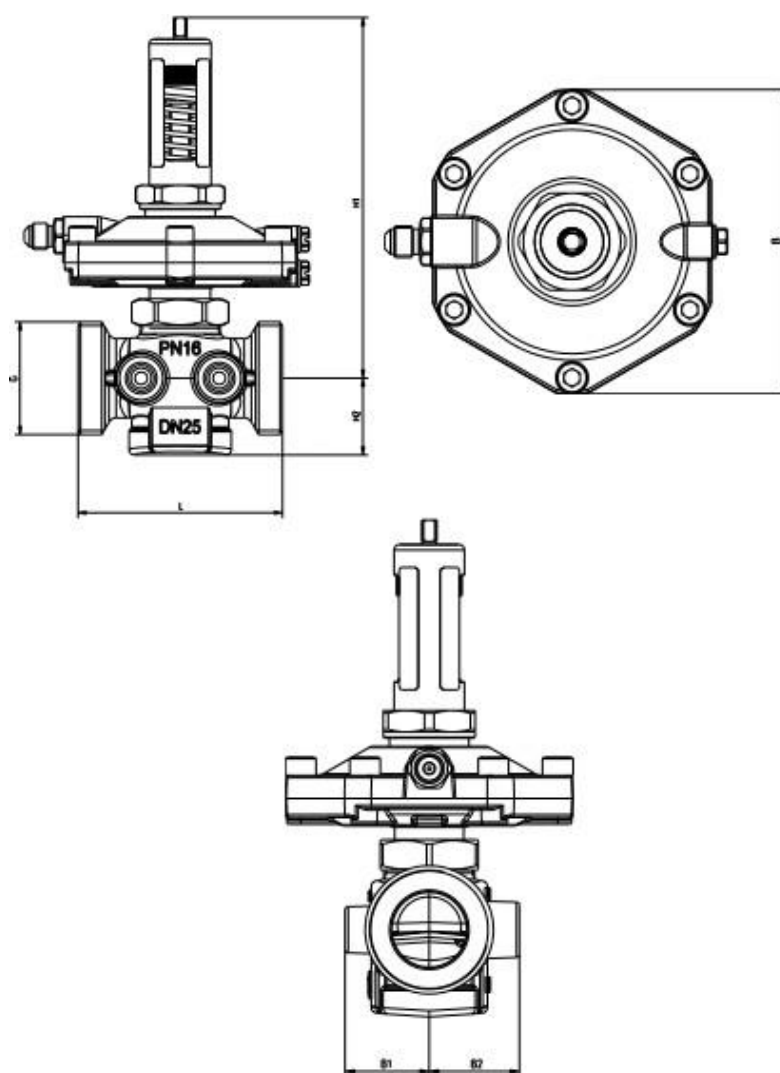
Герц - Регулювальний клапан (4002_4X-6X)
